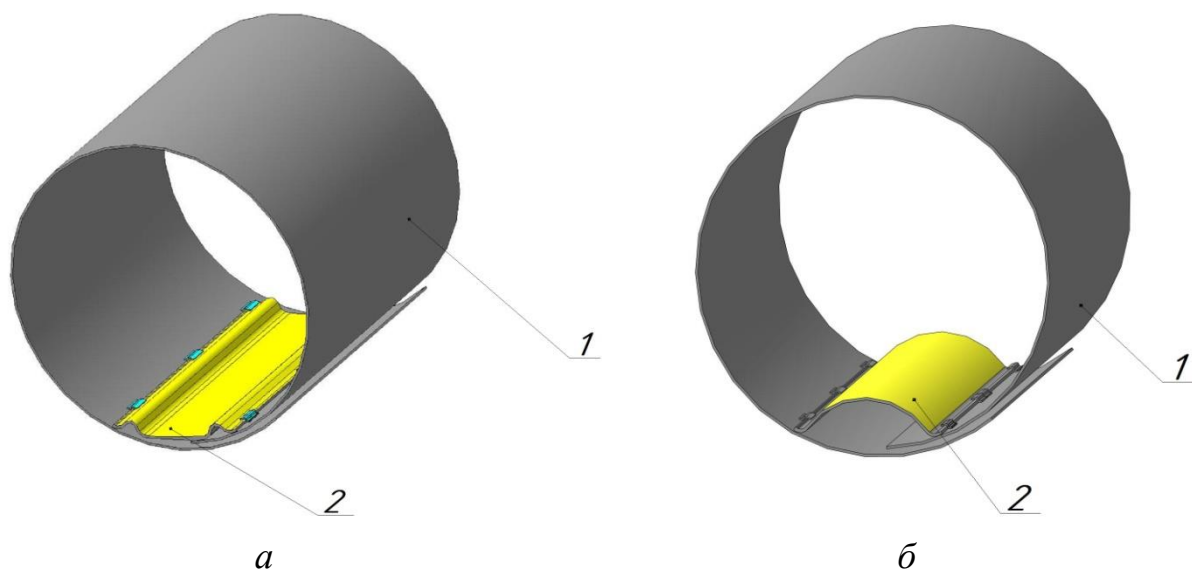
Приклад заготовки 1 для відновлення резервуару з використанням технологічних елементів 2 для деформування заготовки після її розміщення в резервуарі
